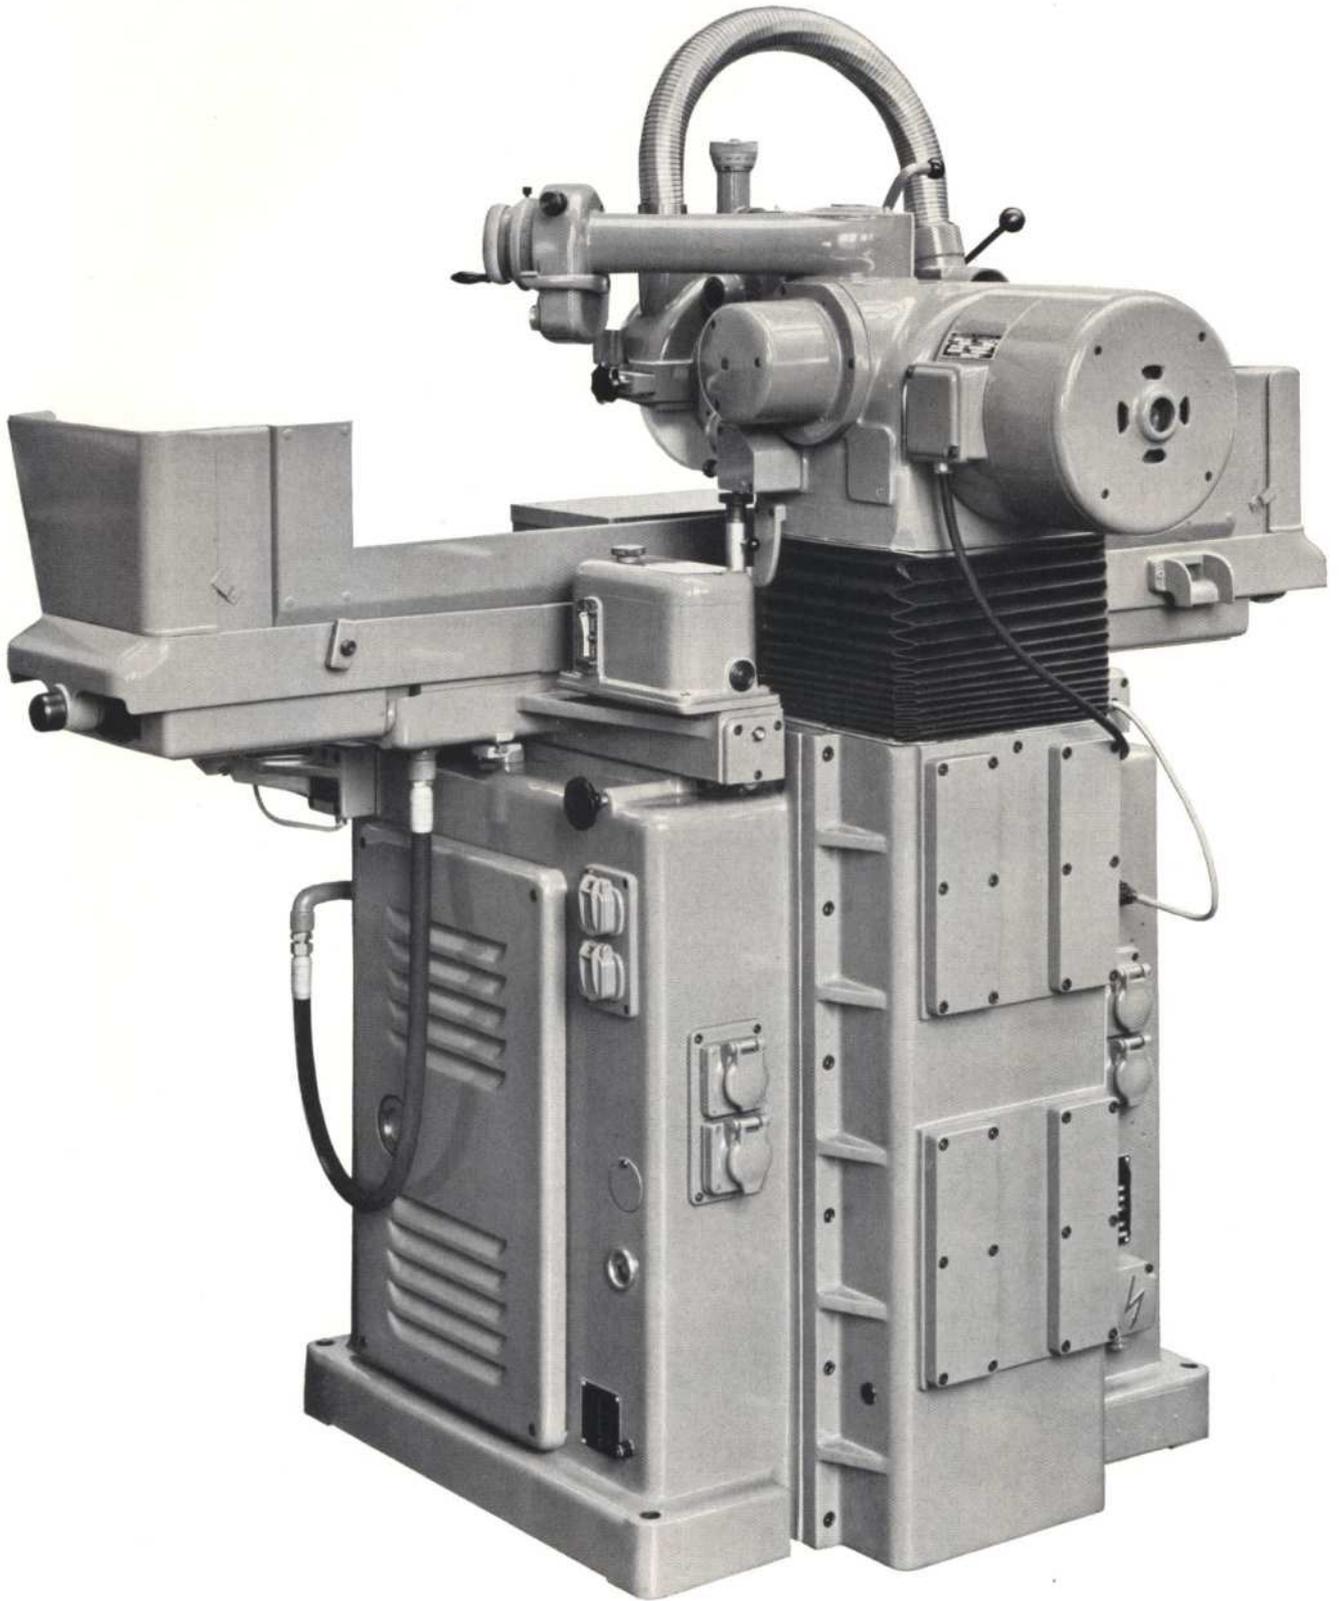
zeigt die Rückansicht der Maschine F 50 mit Regelantrieb
